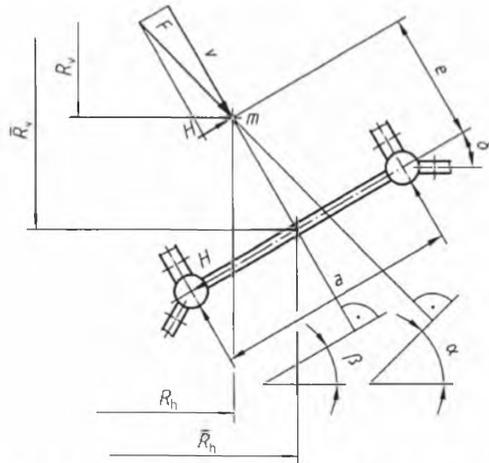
Поперечное сечение рельсов с опорными и направляющими колесами
